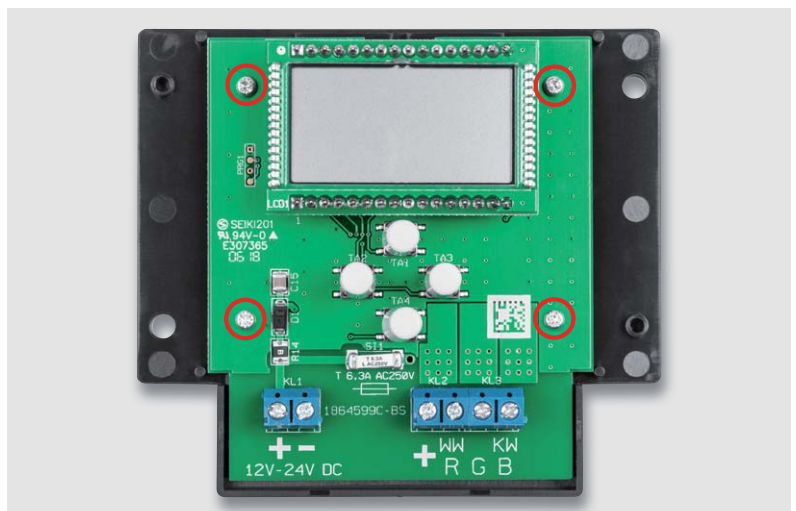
So wird die Hauptplatine mit vier Schrauben im Gehäuseunterteil verschraubt.
